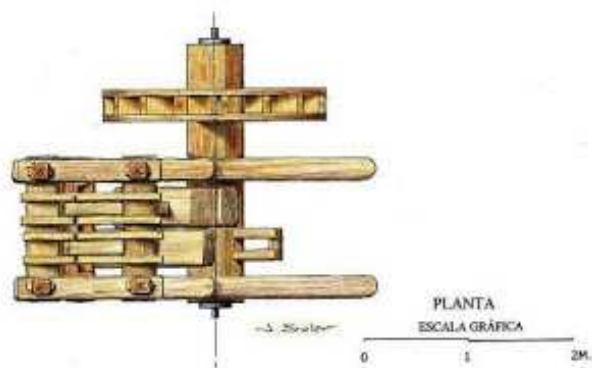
Planta 6.1.5.2.5
